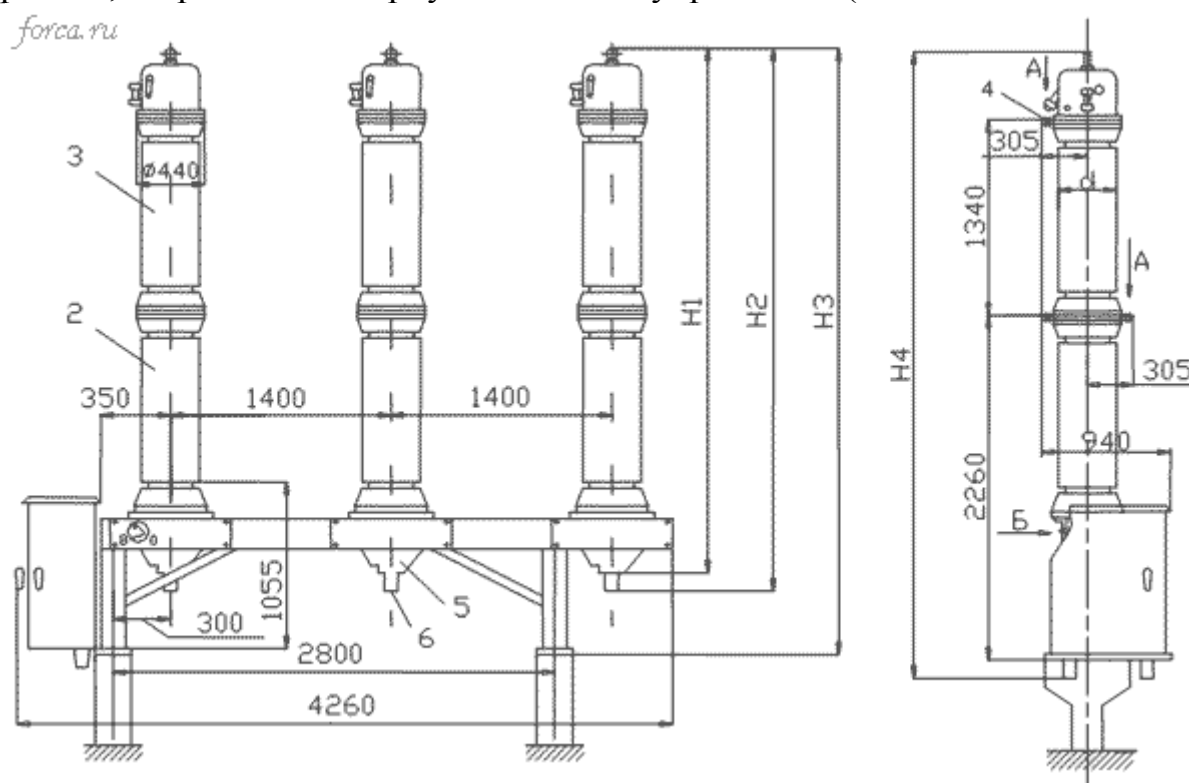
Габаритные, установочные и присоединительные размеры выключателя типа ВМТ-35Б. 1- привод; 2- изолятор опорный; 3- дугогасительное устройство; 4- ввод; 5- механизм управления; 6-подогревательное устройство (для исполнения УХЛ1); 7- рама; 8- указатель положения В и О; 9- кабельная муфта; 10- знак заземления; 11- болт заземления М16-8д.; 12- опора рамы.
